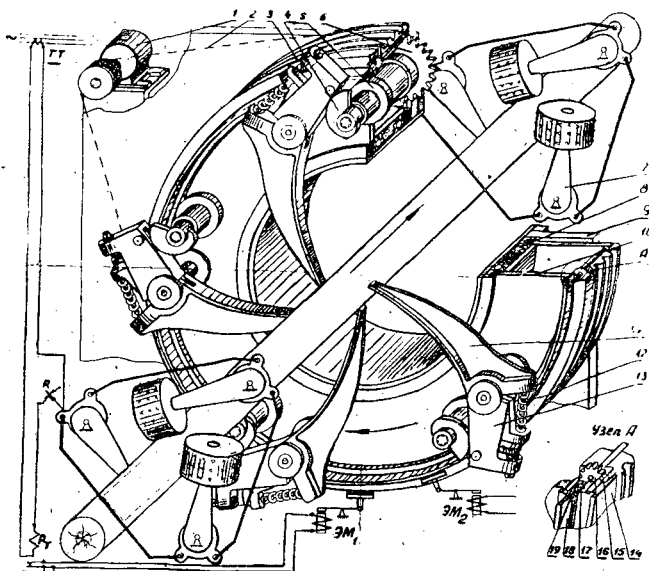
Аксонометрическая схема универсального окорочного станка.
